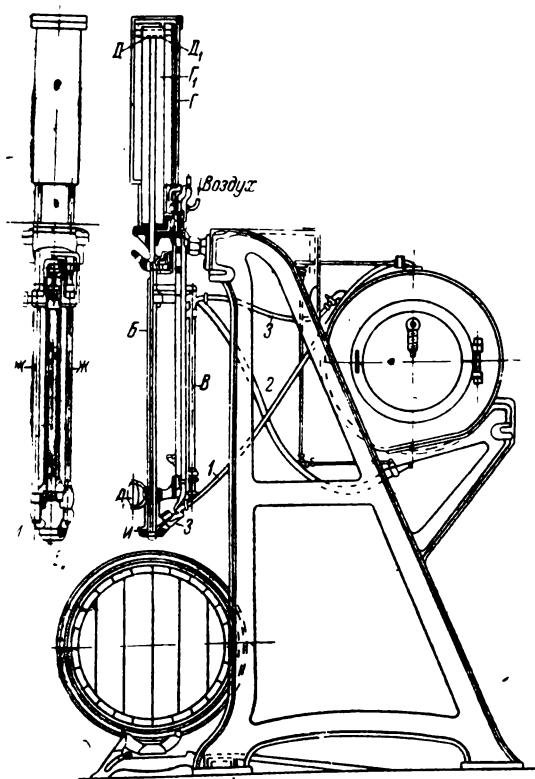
Автоматический наполнитель бочек, работающий сжатым воздухом
